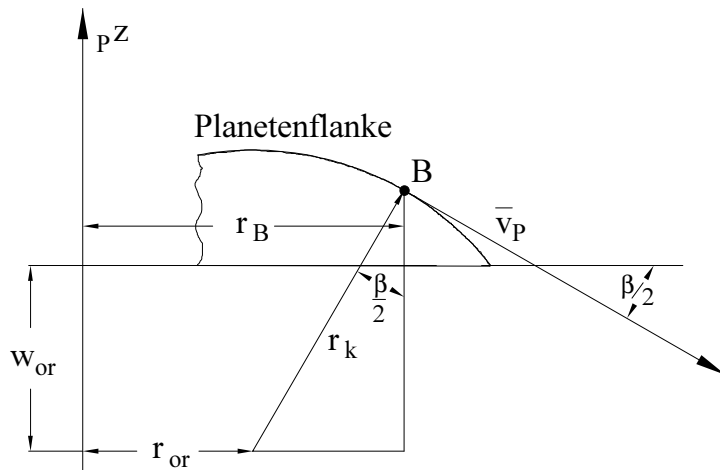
Flankenvektor im Meridianschnitt der Planetenflanke
